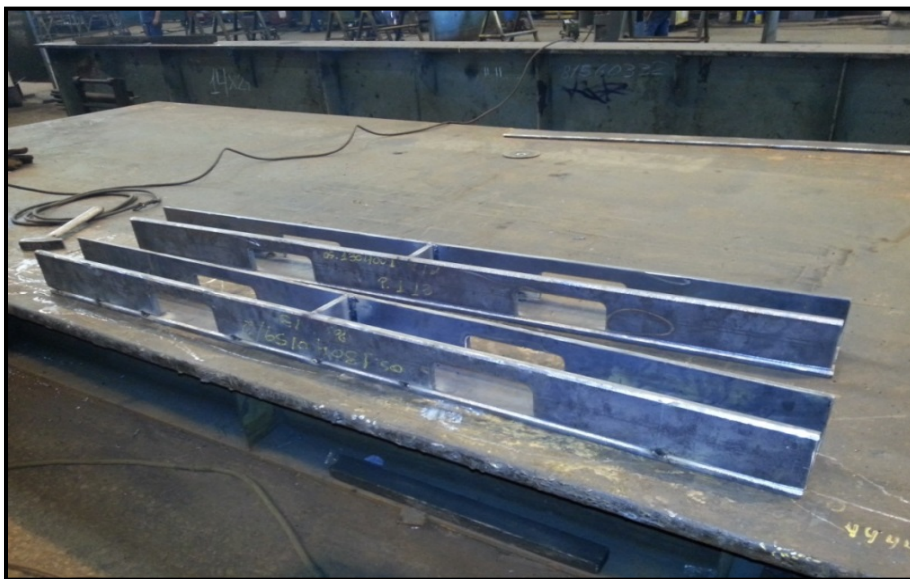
Vigas ponteadas preparadas para enchimento de solda.
